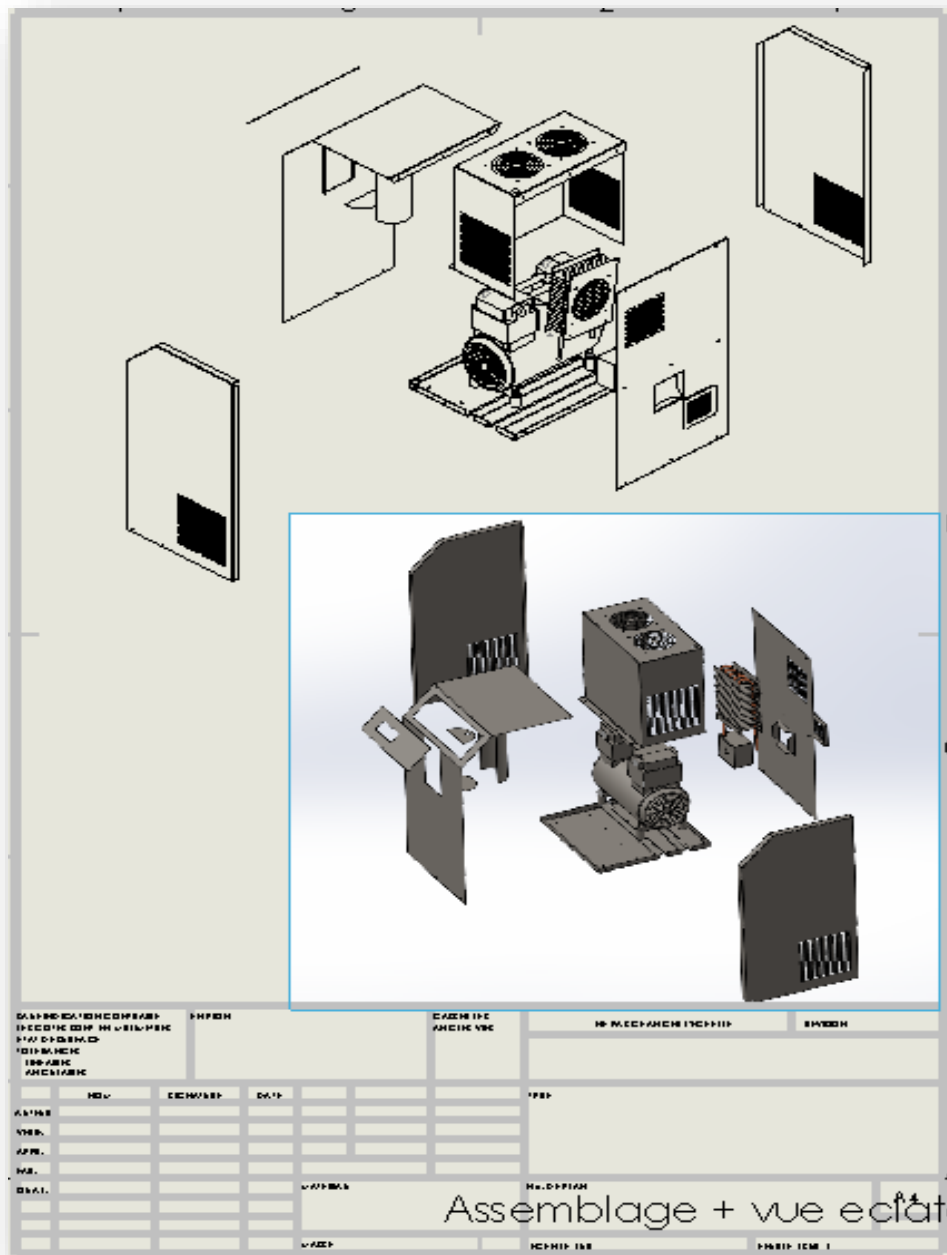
Mise en plan de la vue éclatée de l'assemblage avec la CAO 3D.
